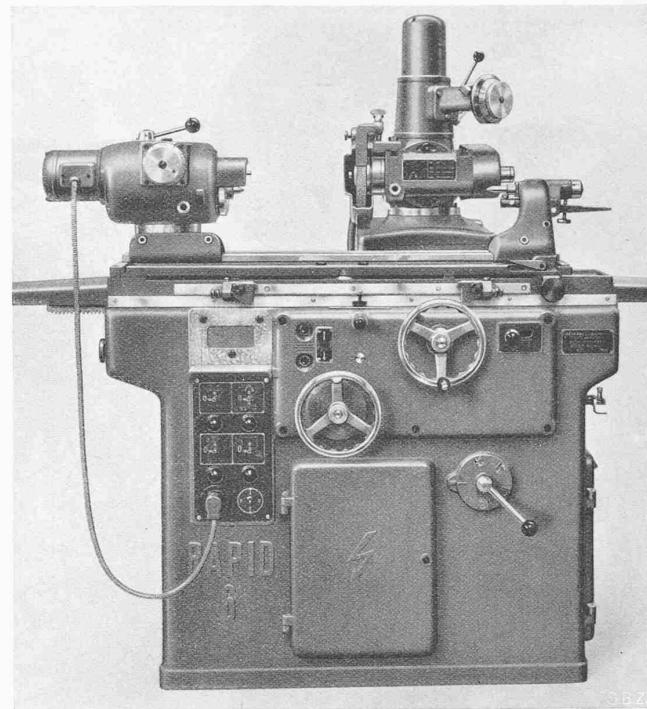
Universal-Werkzeug-Schleifmaschine der «Rapid» A. G. Uster
